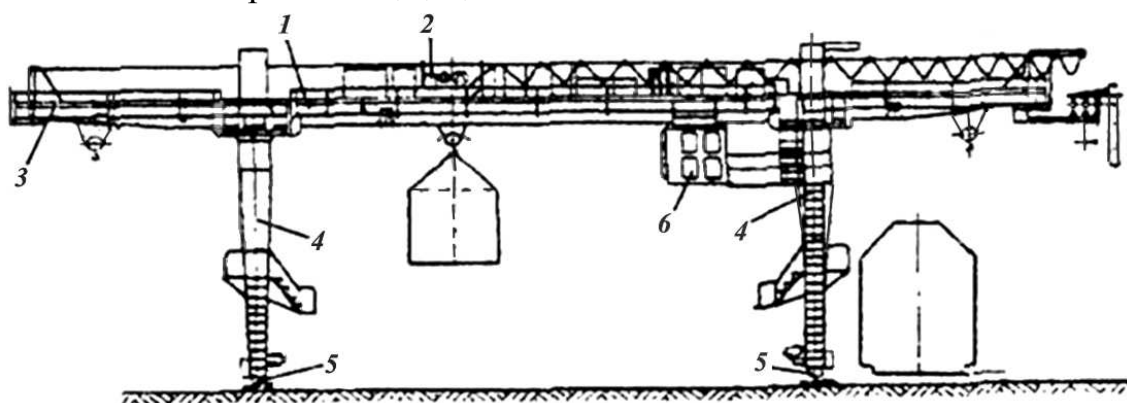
Схема козлового крана для погрузки-выгрузки контейнеров:
